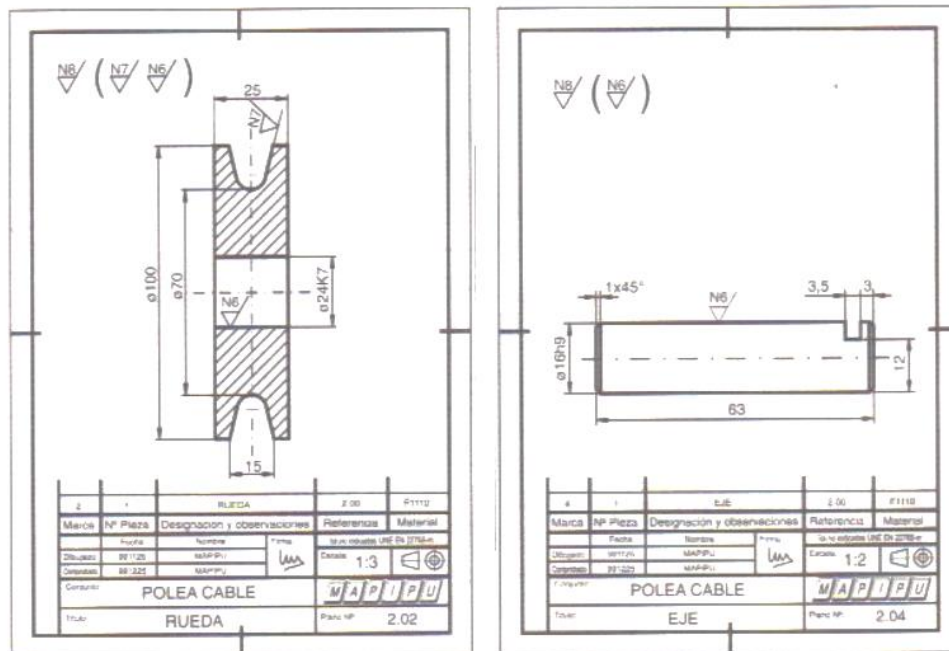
Planos de conjunto de la rueda y eje de la polea cable
